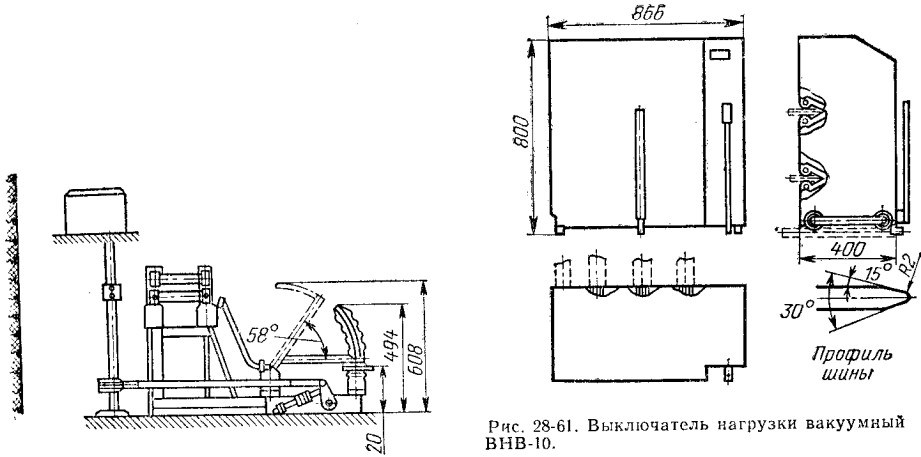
Выключатель нагрузки вакуумный ВВ-10.
